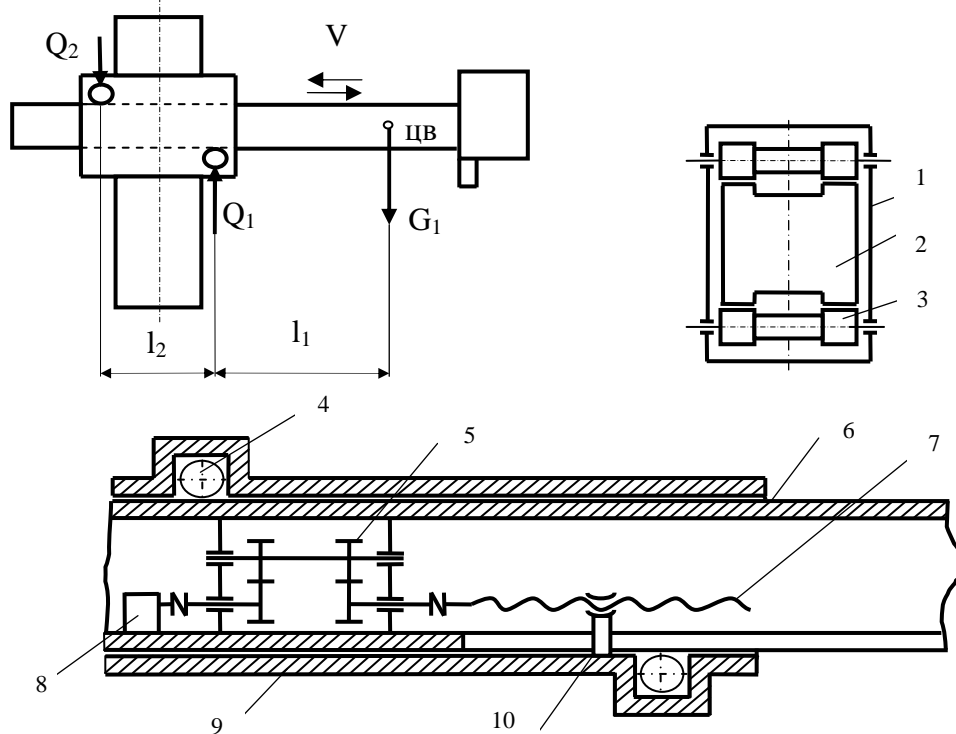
Розрахункова та конструктивна схеми механізму висування штанги: 1,9 – корпус каретки; 2,6 – штанга висувна; 3,4 – ролик; 5 – редуктор; 7 – гвинт ходовий; 8 – двигун; 10 – поводок гайки.
